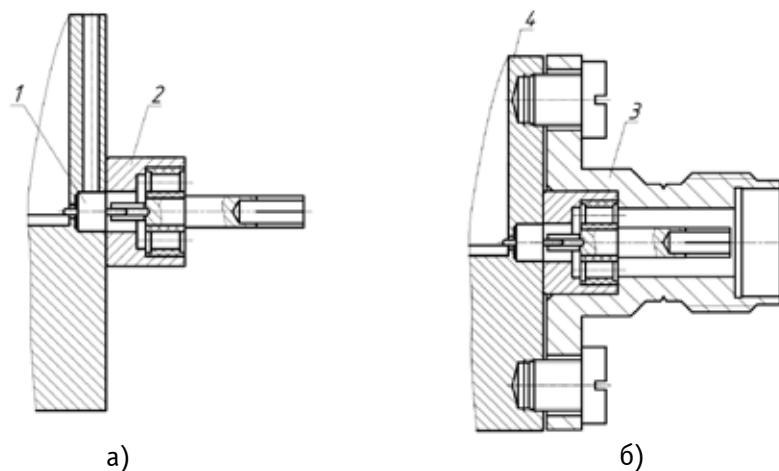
Установка центрального проводника (а) и корпуса (б) фланцевого соединителя
